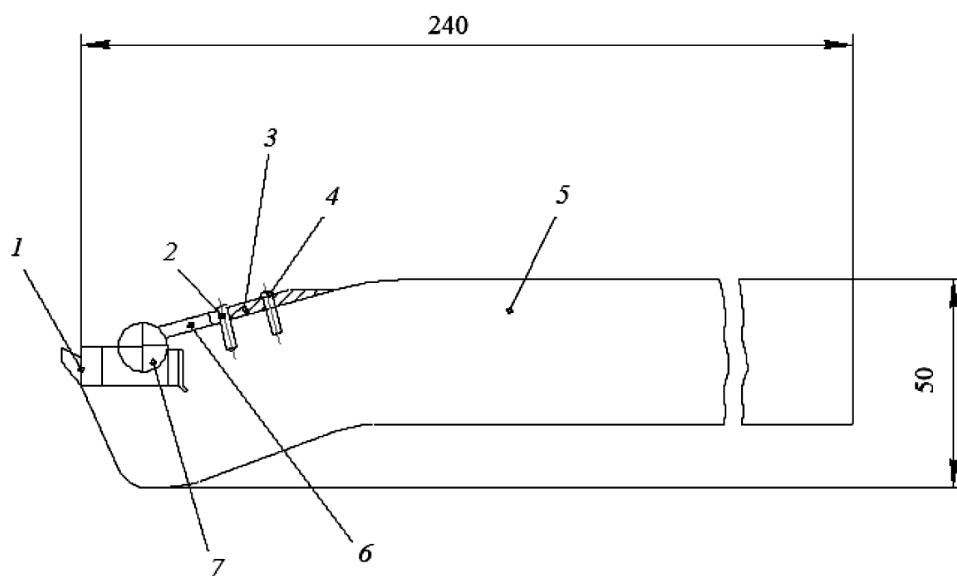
Експериментальний стругальний різець: 1 — різальний елемент; 2 — штифт; 3 — фіксуюча пластина; 4 — гвинт; 5 — тримач; 6 — підпора; 7 — циліндричний валець
